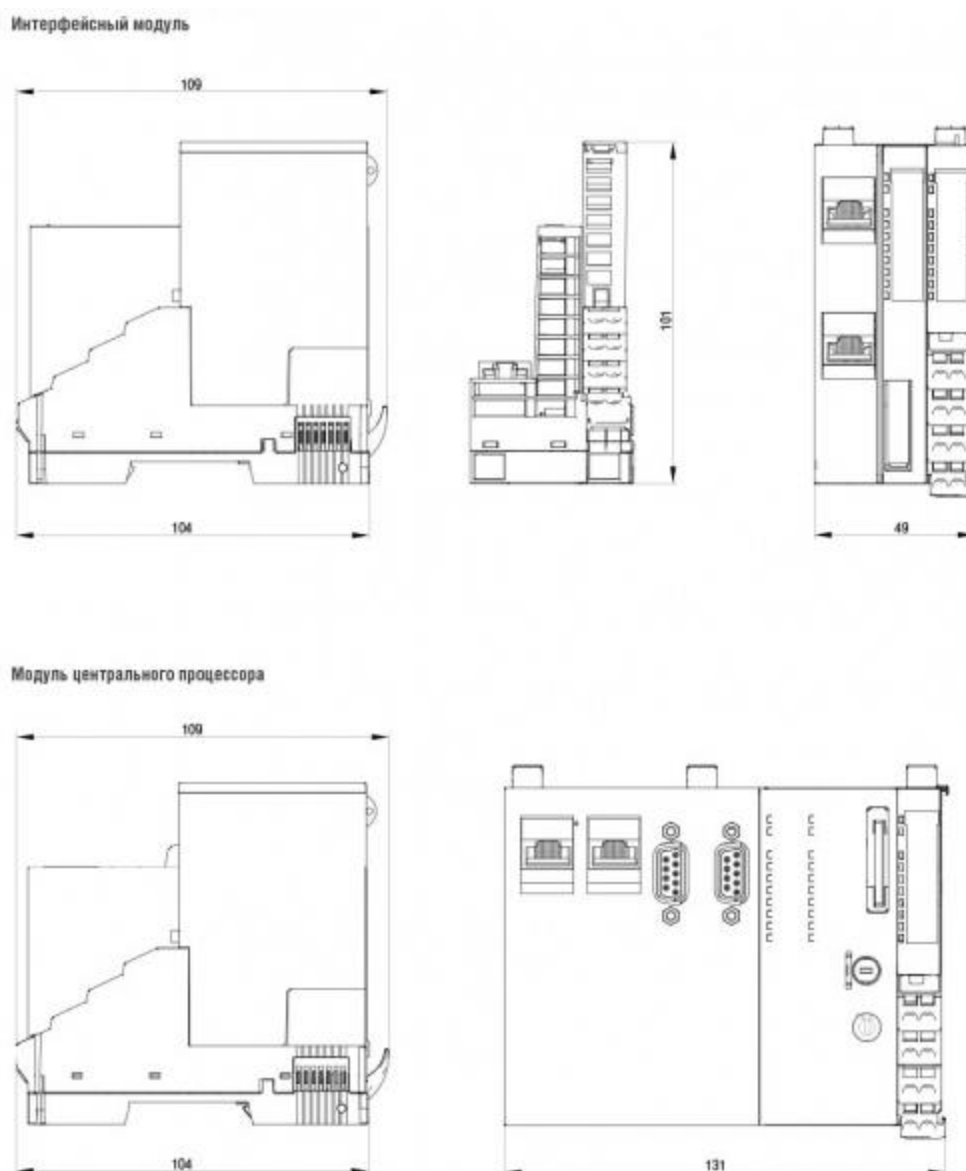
Габаритные размеры контроллера REGUL-R200
